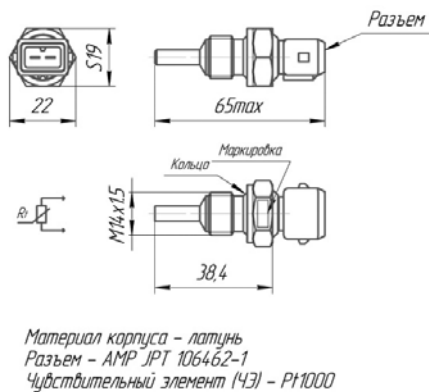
Чертеж и габаритные размеры датчика ЧЭПТ-3-БР
